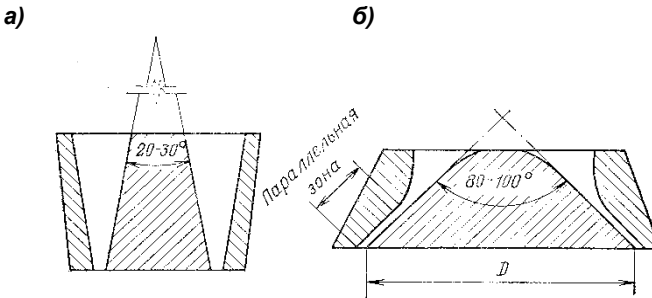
Профили рабочего пространства конусной дробилки крупного дробления (а) и дробилки среднего и мелкого дробления (б)
